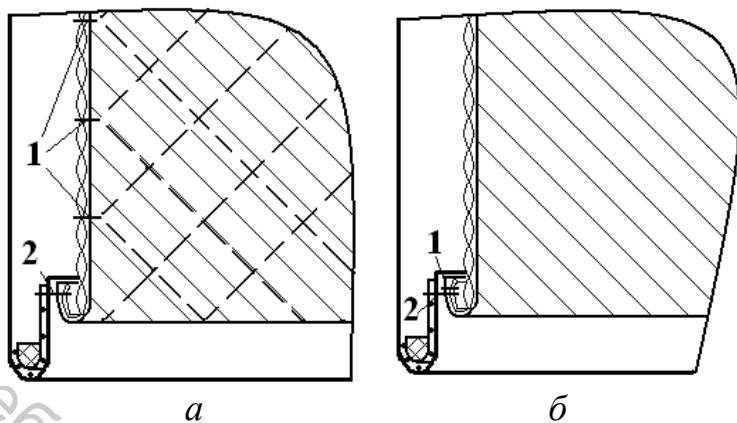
Соединение утепляющей прокладки и подкладки с рукавом
